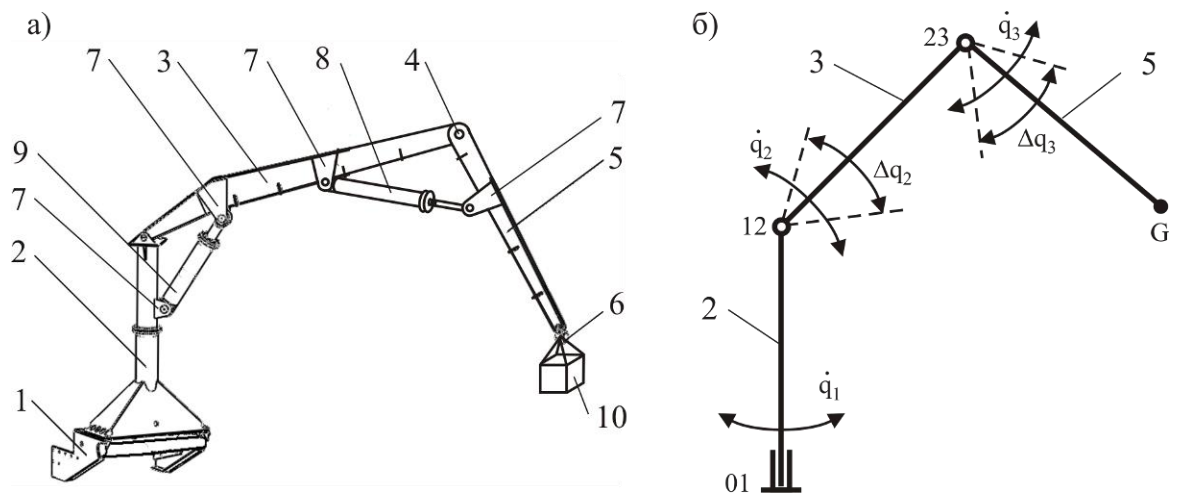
Триважільний гідравлічний крановий маніпулятор: а – конструкція (1 – опорна конструкція; 2 – поворотна колонка; 3 – стріла; 4 – шарнірний перехід сусідніх ланок; 5 – ручка; 6 – вантажно-розвантажувальний орган; 7 – елементи кріплення; 8 – силовий гідродвигун механізму обертального переміщення палиці; 9 – силовий гідромотор хитного механізму стріли; 10 – вантаж); б – кінематична схема
